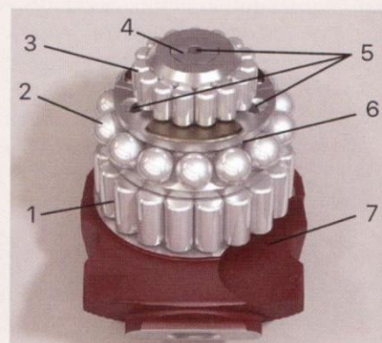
Система опоры шарошечных долот: 1 – внешний роликовый подшипник; 2 – шарикоподшипник; 3 – внутренний роликовый подшипник; 4 – подпятник; 5 – воздушные каналы; 6 – торцевой подшипник скольжения; 7 – щелевое отверстие для выпуска воздуха.
